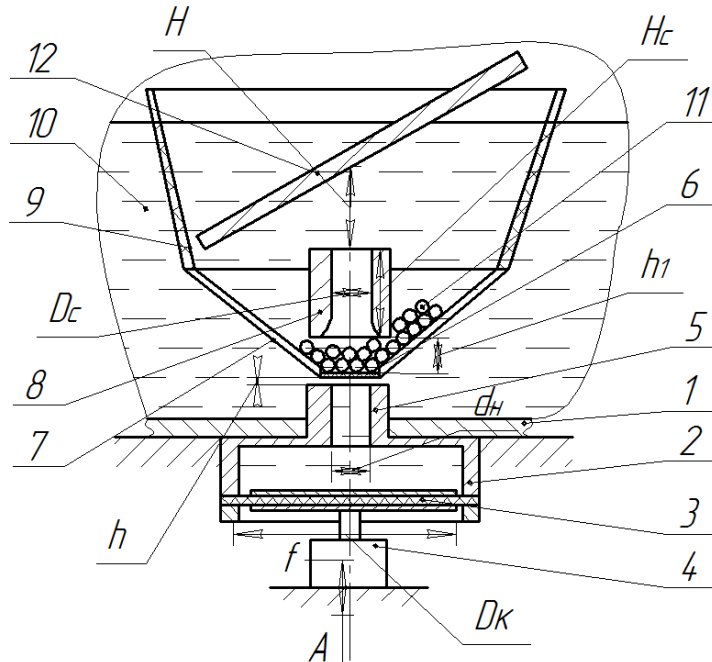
Схема роботи вібраційної машини для очищення та мийки деталей машин у пульсуючому потоці рідини з твердими частинками: 1 – корпус ванни; 2 – камера пульсації; 3 – мембрана з дисками; 4 – вібропривід; 5 – насадок; 6 – сітка; 7 – короб для збору твердих частинок; 8 – сопло; 9 – сітка; 10 – миюча рідина; 11 – тверді частинки; 12 – поверхня, що очищується; H – відстань від сопла до поверхні, що очищується; H_c – висота сопла; h – відстань від насадка до сітки; h_1 – відстань від сітки до сопла; d_n – діаметр насадка; D_k – діаметр камери пульсації; D_c – діаметр сопла; f – частота коливань віброприводу; A – амплітуда коливань віброприводу
